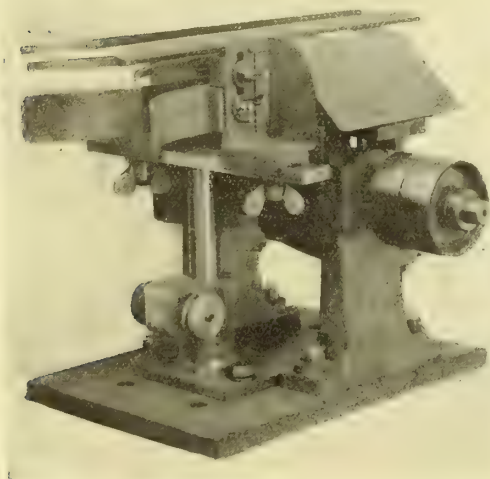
Fig. E. — Vue perspective de la machine de M. H. Vollet. Ensemble de la machine munie de ses protecteurs.
